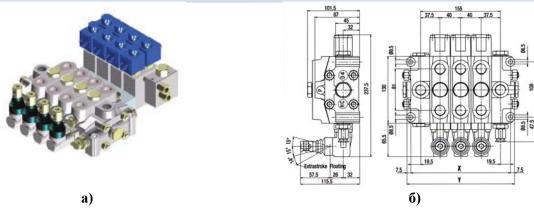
Общий вид (а), габаритные и присоединительные размеры б) распределителя НС-D4.
